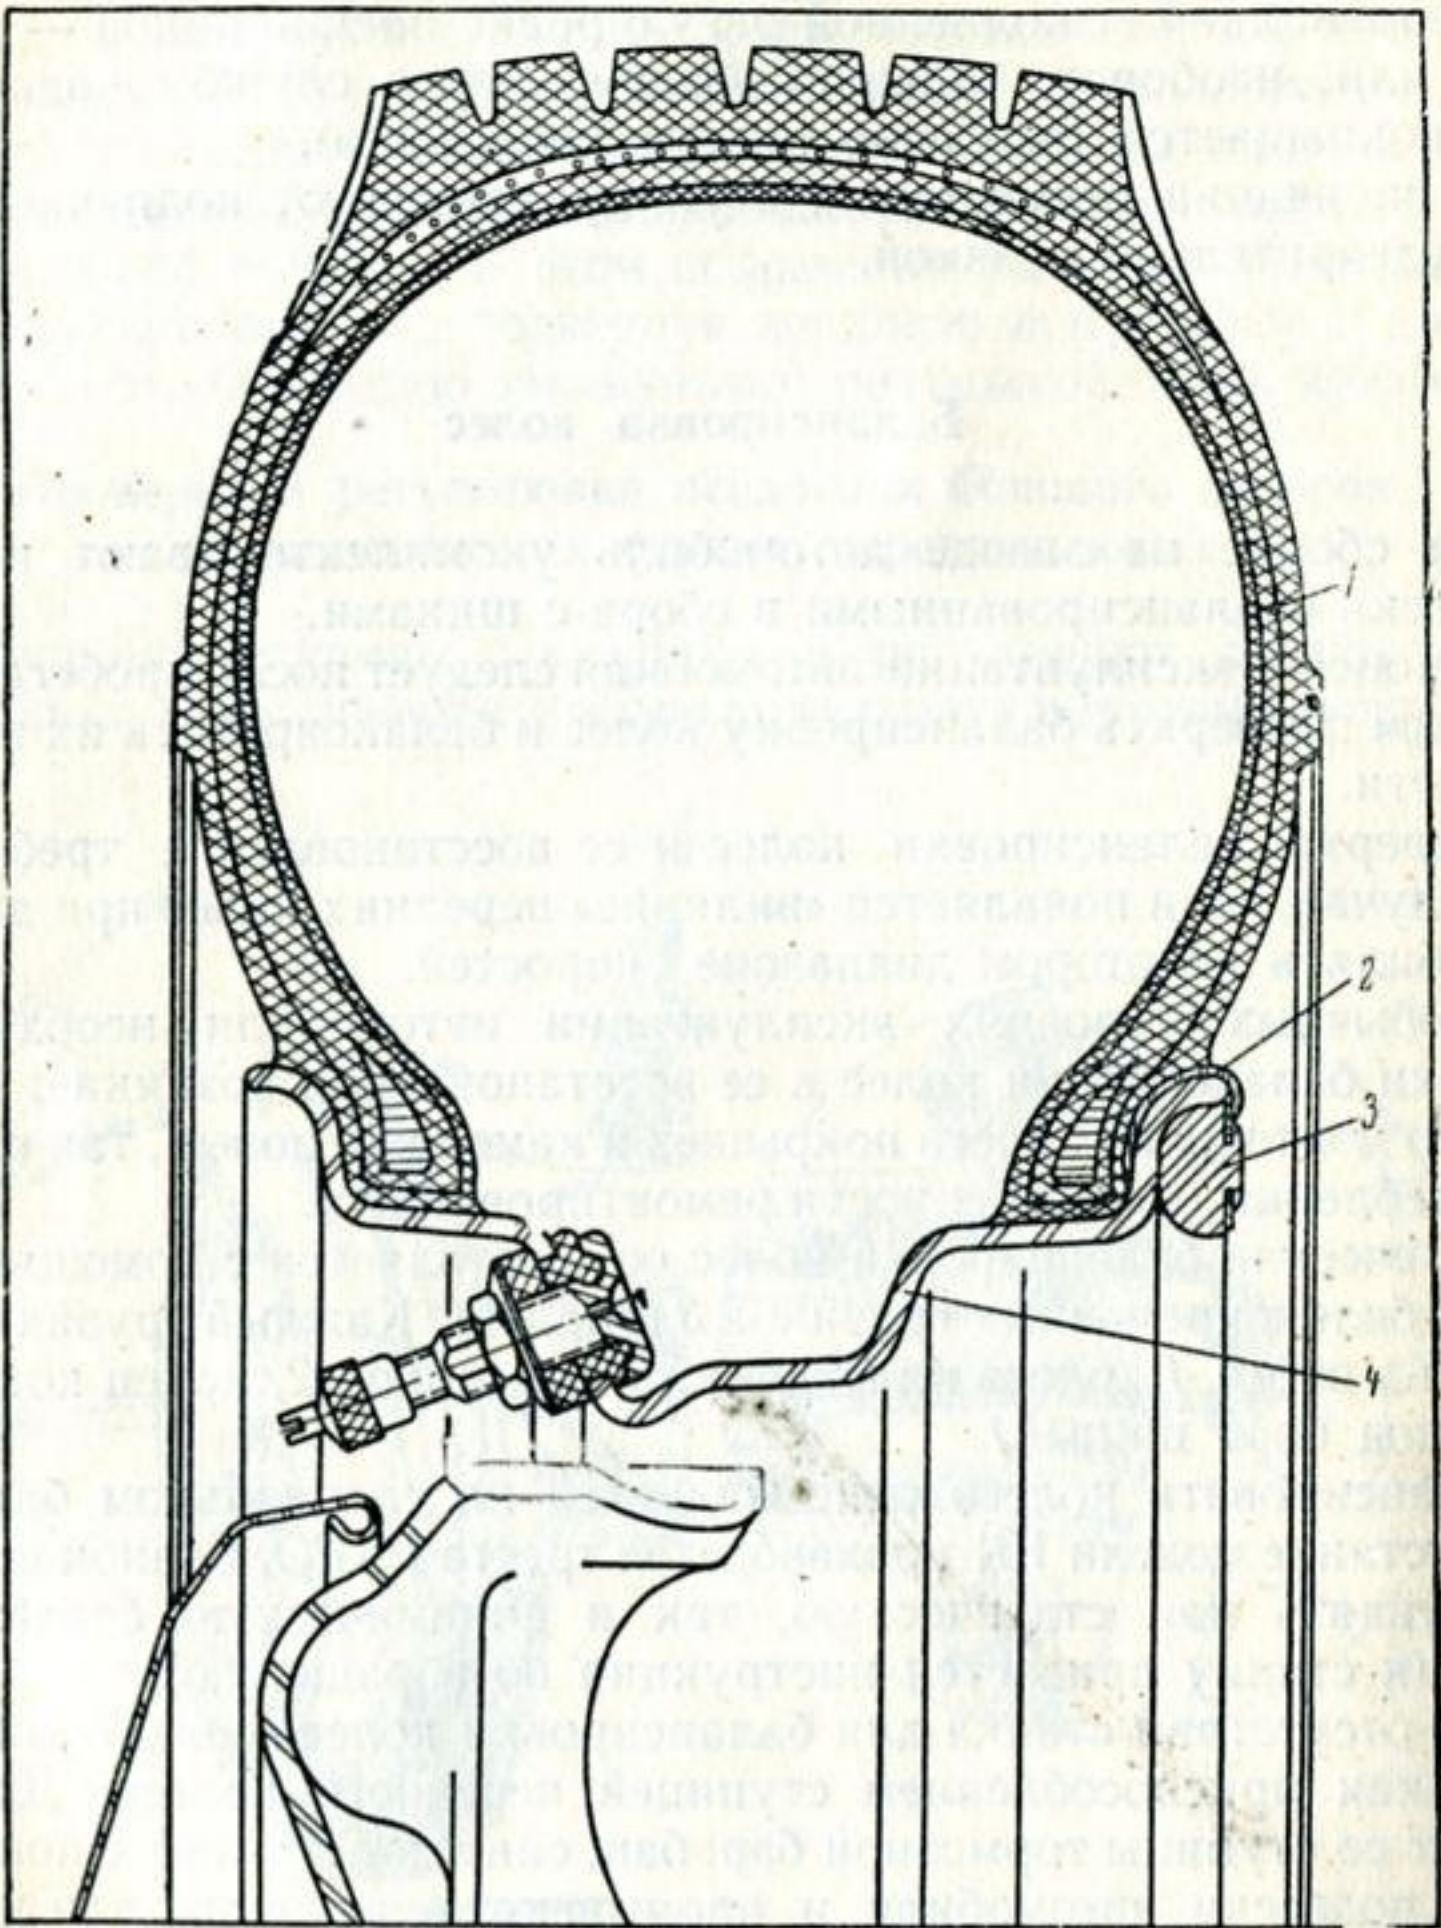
Крепление балансировочного грузика на ободе колеса:
